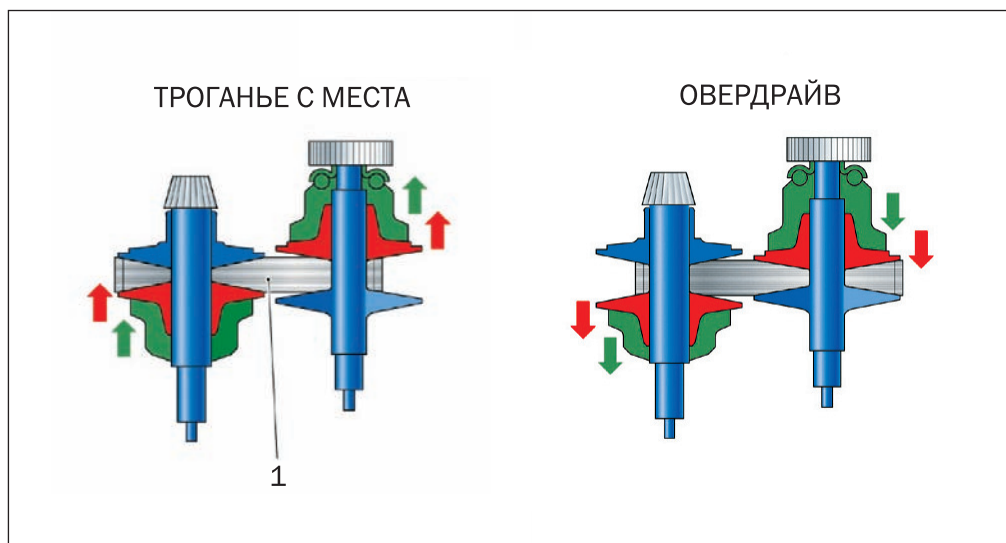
Схема работы вариатора Multitronic: 1 — цепь
